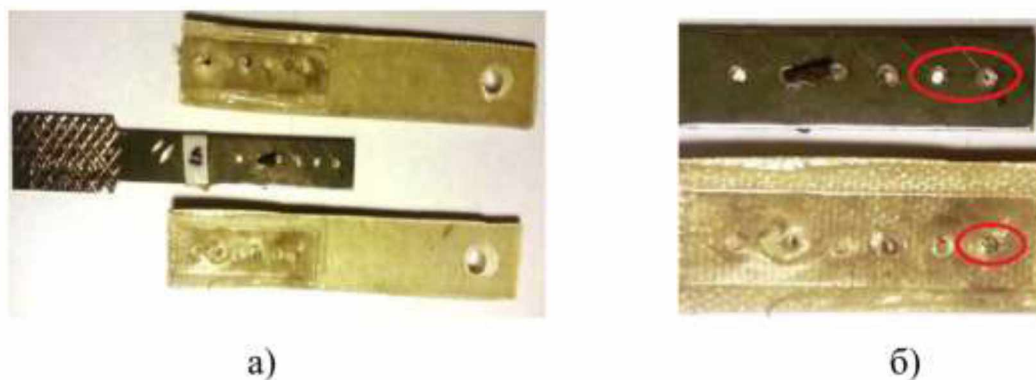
Зразок металокомпозитного з'єднання після руйнування – (а); вид руйнування (зріз з вириванням КЕ) – (б)
